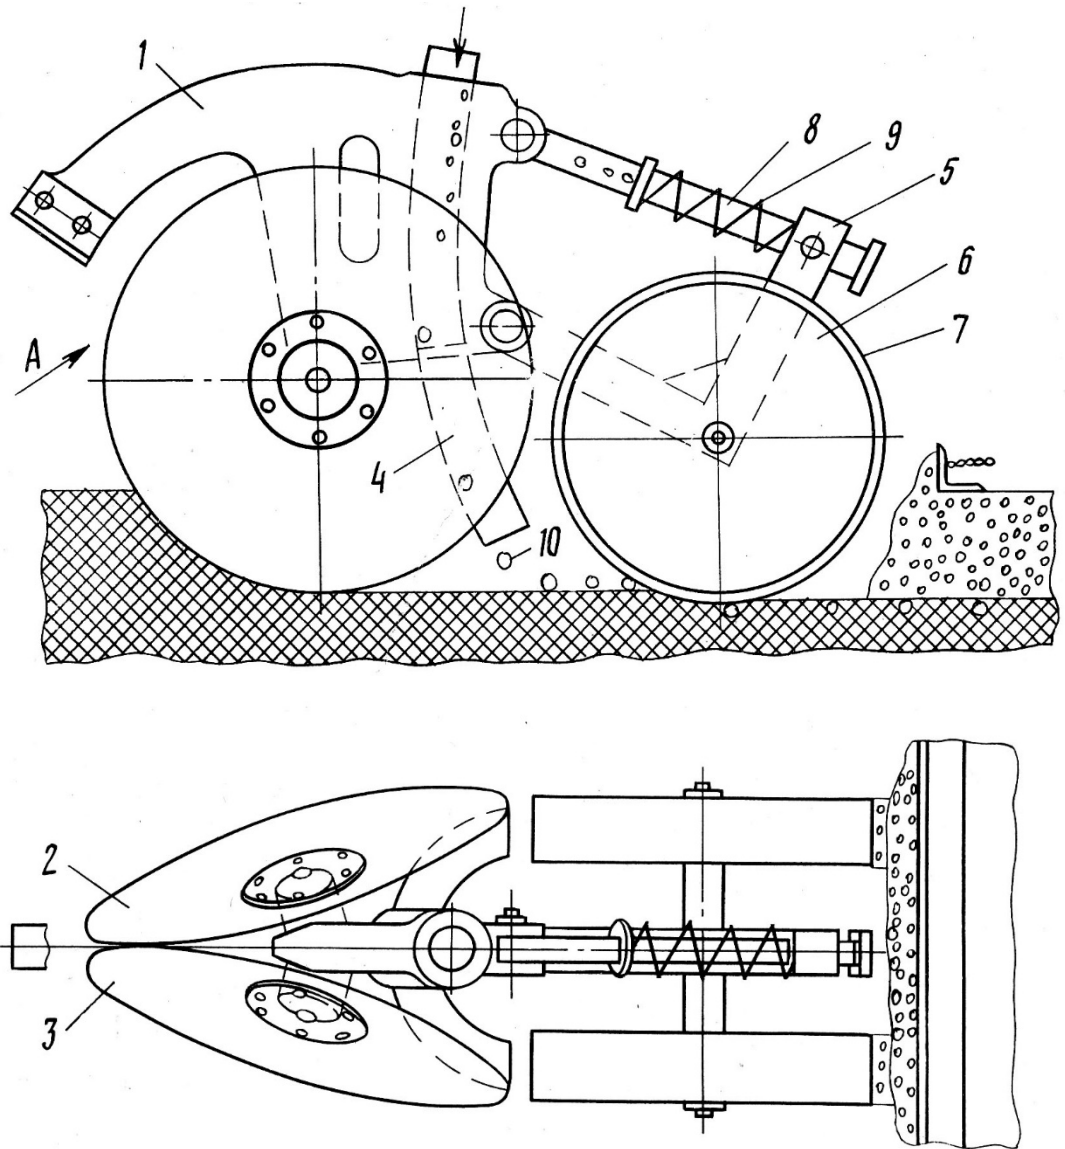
Схема сошника для смугової сівби: 1 – корпус; 2, 3 – диск;
